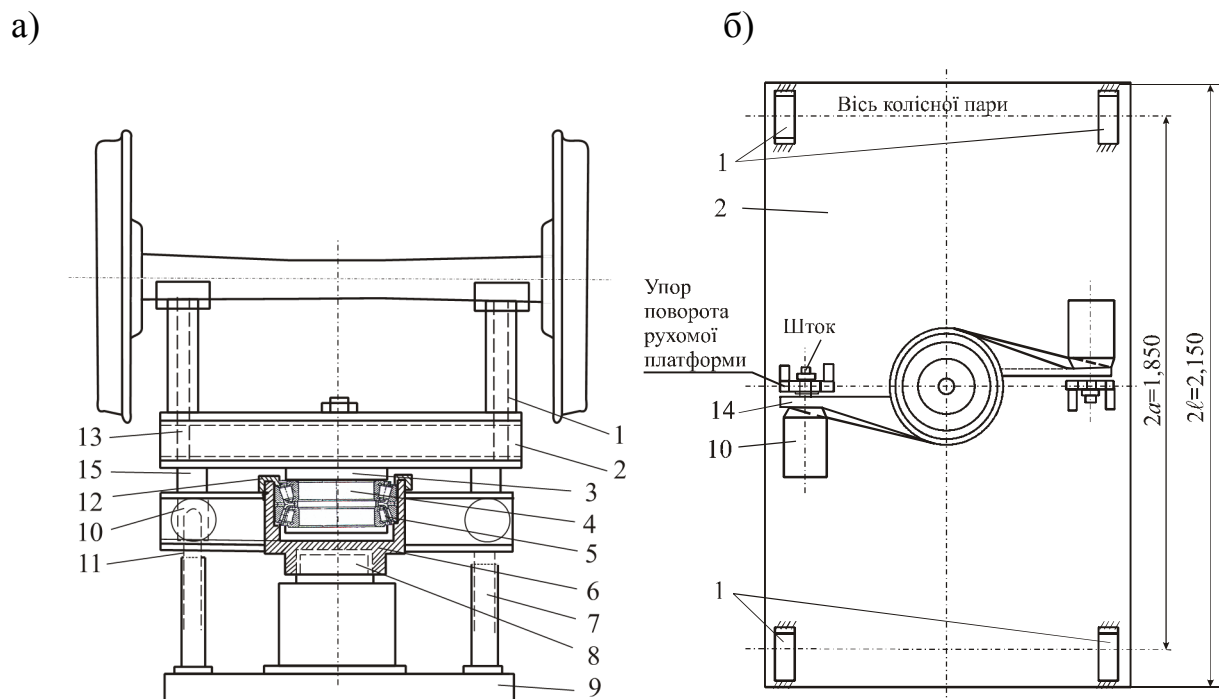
Общий вид станда и механизма нагрузки
